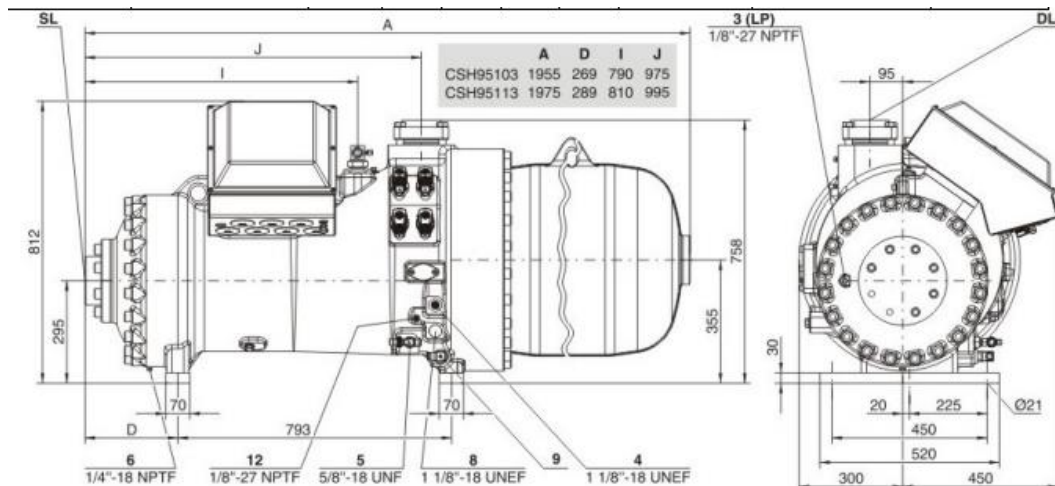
Загальний вигляд компресора Bitzer CSH95113-320Y
